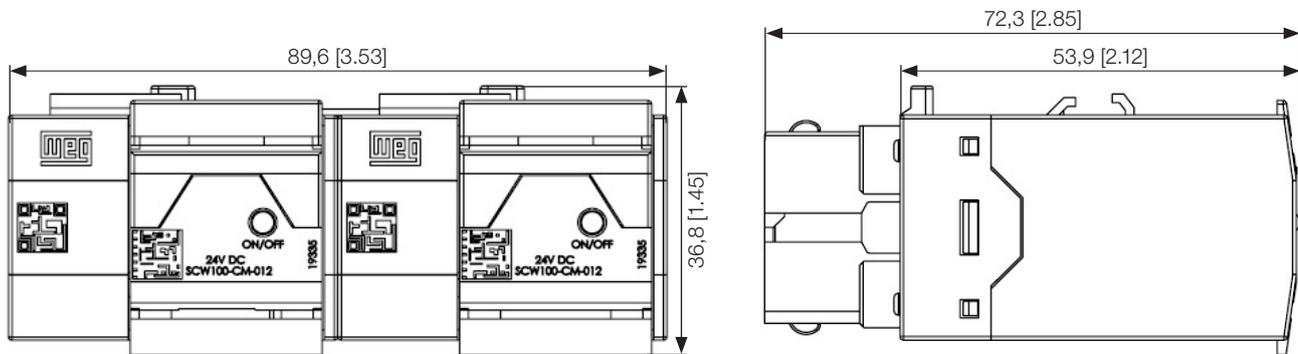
Dimensões do Módulo de Conexão Partida Reversora (CM-002) em mm [in]
